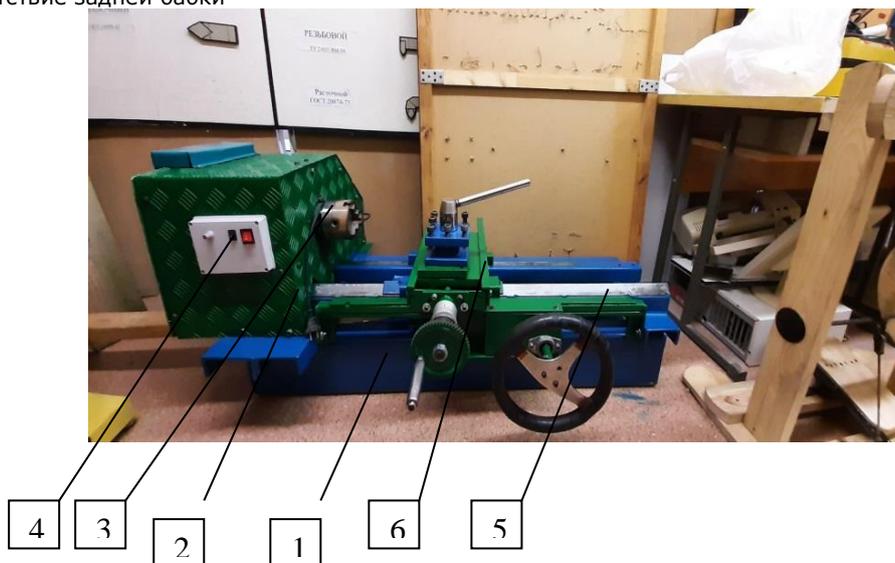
Внешний вид станка: 1-Станина, 2-Передняя бабка, 3-Панель управления, 4-Трёхкулачковый патрон, 5-Продольные салазки, 6-Суппорт
